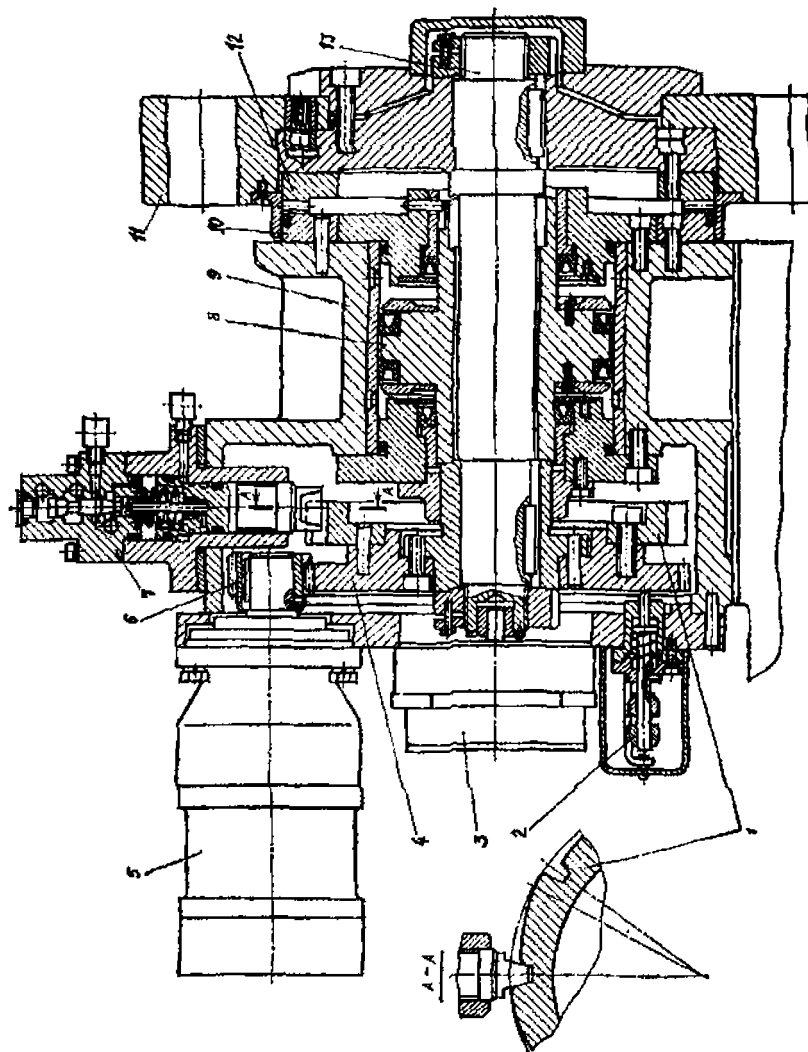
Конструкция гидрофицированной револьверной головки токарного станка
